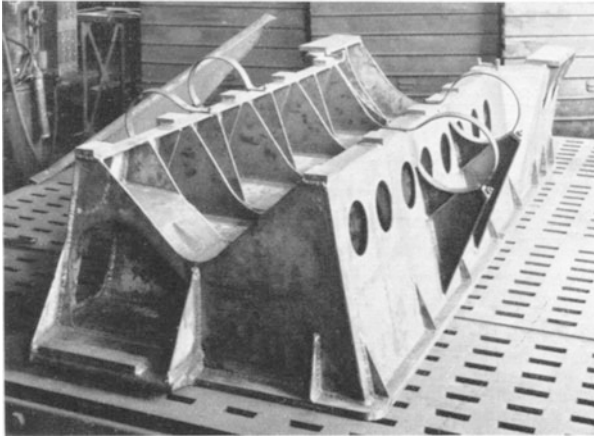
Geschweißtes Dieselmotorenstell.
